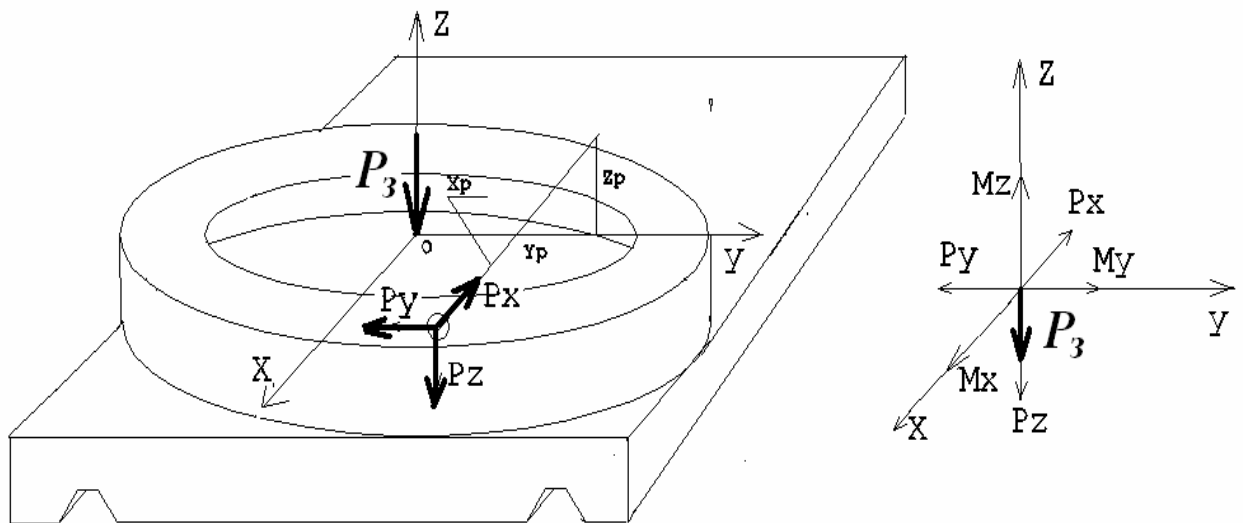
Розрахункова схема зубчастого стику механізму фіксації
